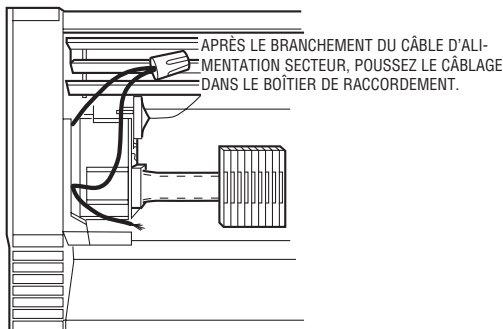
Câblage au travers de l'ouverture de boîtier de raccordement
